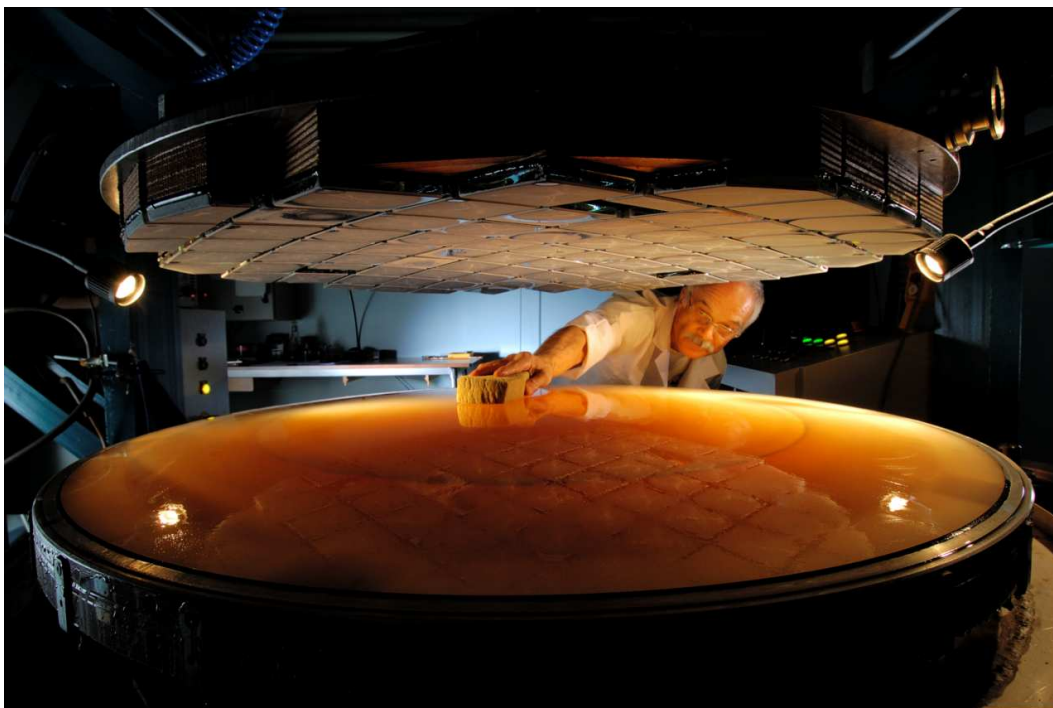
Machine de polissage de 1.6m durant l'opération de rodage du plateau par un outil annulaire.
